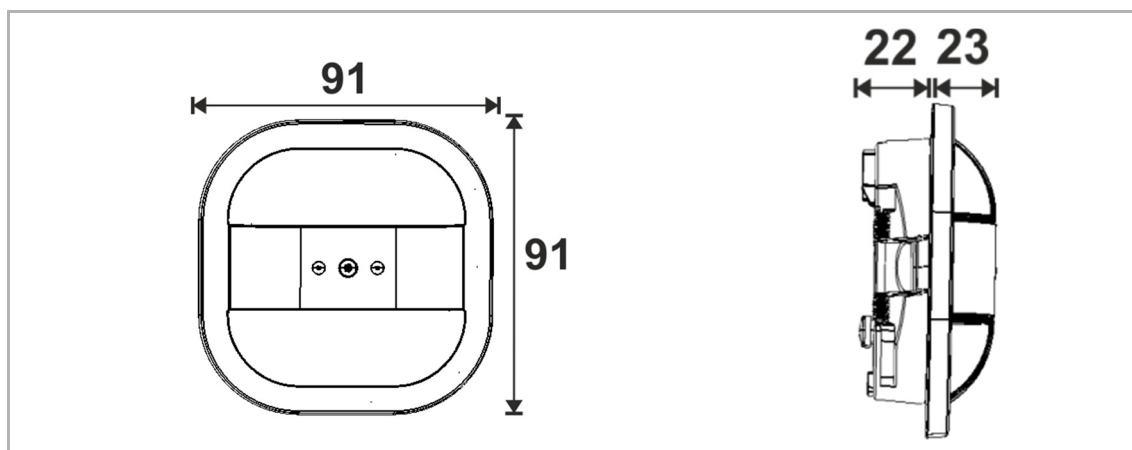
Размеры датчиков Busch-Präsenzmelder KNX / Busch-Präsenzmelder Premium KNX
